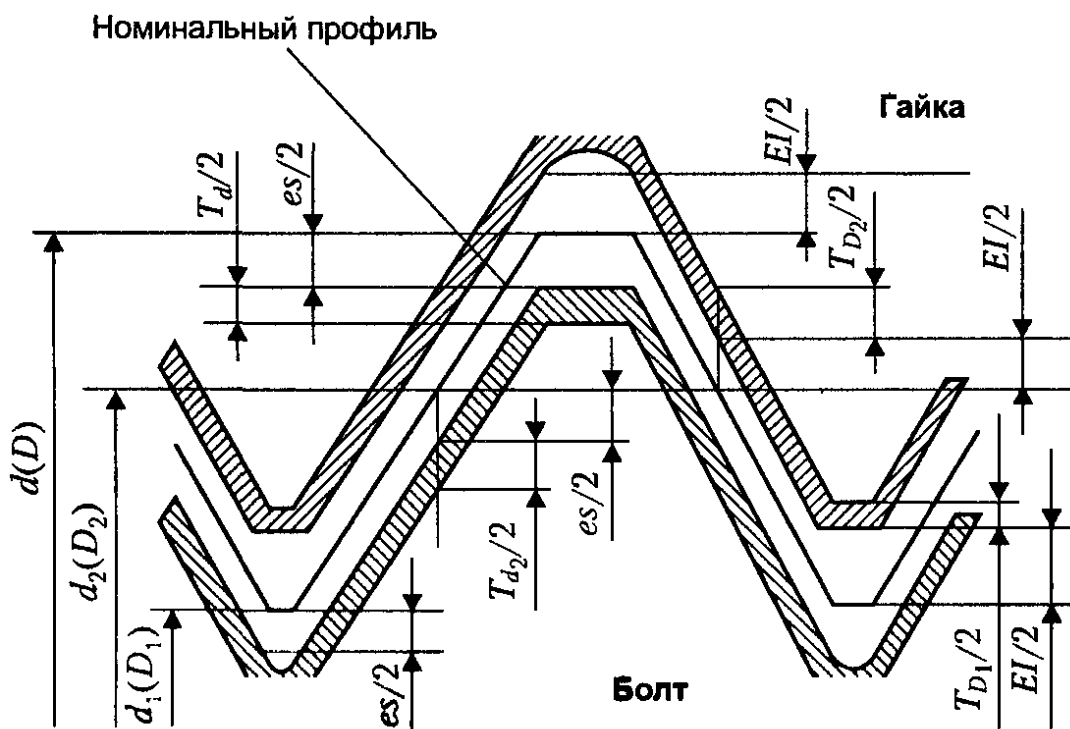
Расположение полей допусков метрической резьбы при посадке с зазором
